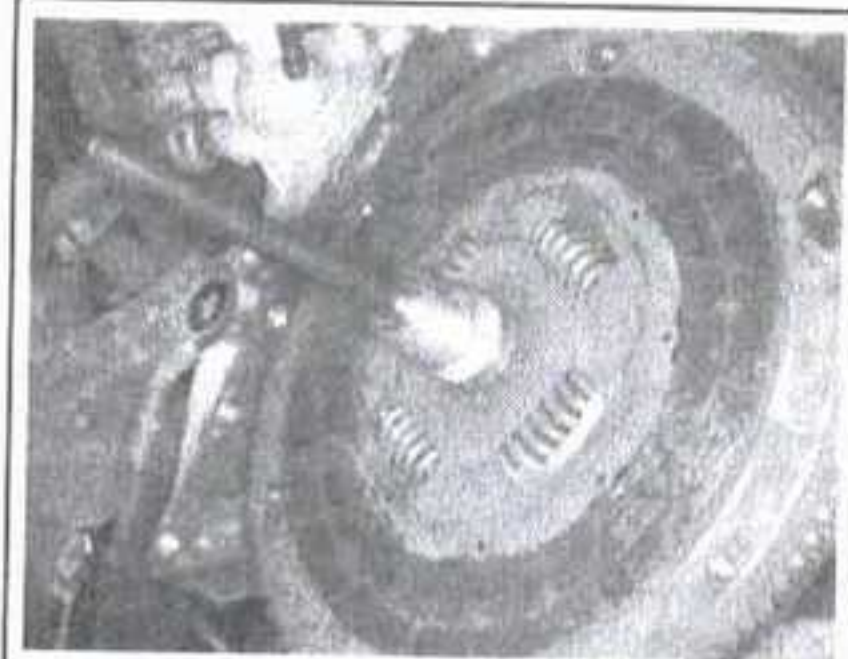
Так должен выглядеть инструмент для выравнивания сцепления после его вставки в направляющий подшипник
